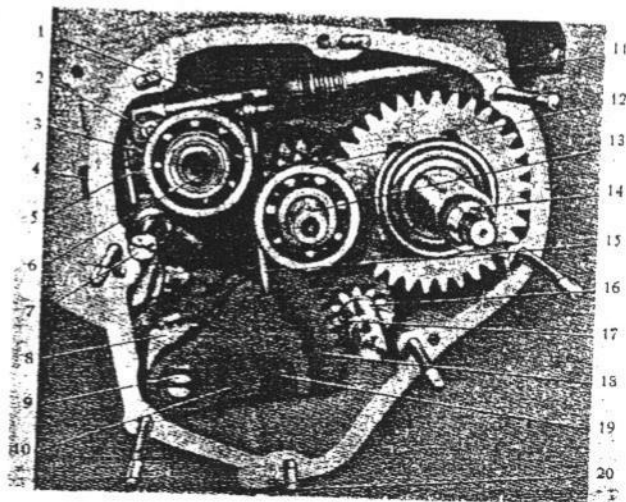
CARTER DE BOÎTE DANS COUVERCLE
